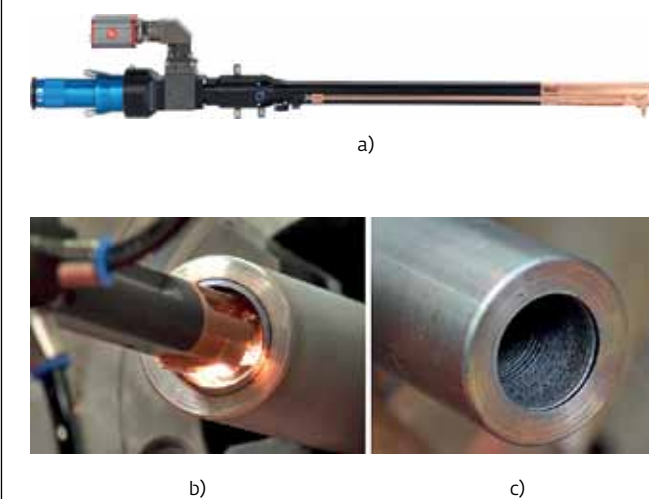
Головка для наплавки в труднодоступных местах: а) – общий вид; б) – процесс восстановления внутренней цилиндрической поверхности; в) – поверхность после обработки
